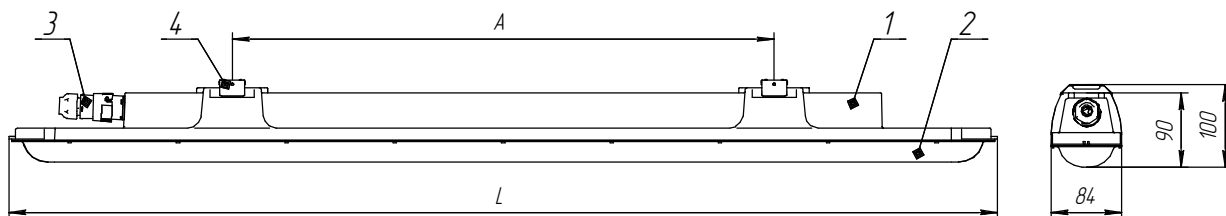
Внешний вид и габаритные размеры светильника серии ДСП51 Leader
